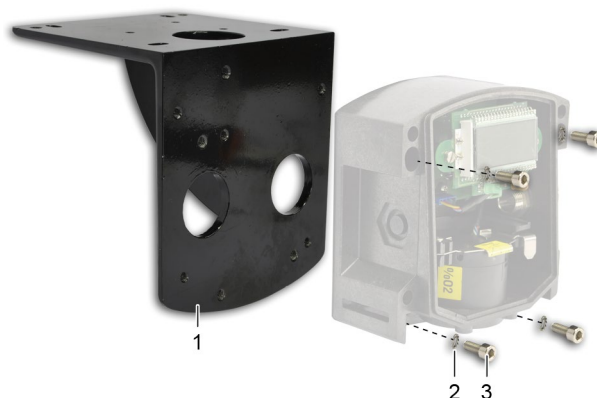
fixation au plafond à l'aide d'une équerre. Les plans de fixation sont identiques à ceux de la fixation murale.
